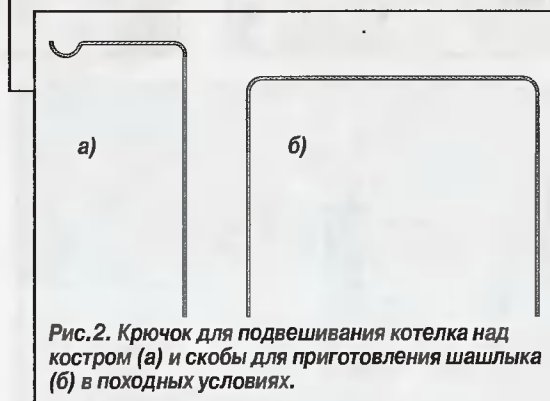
Крючок для подвешивания котелка над костром (а) и скобы для приготовления шашлыка (б) в походных условиях.
